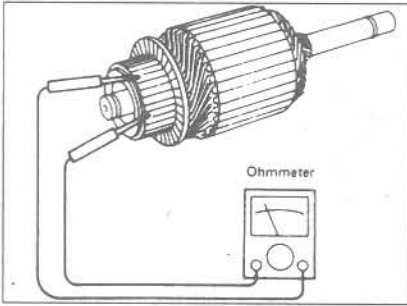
Проверка обмоток якоря (Глава 10)
